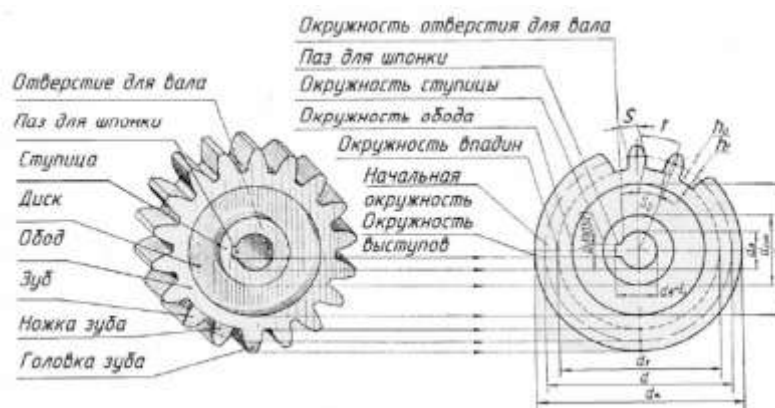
Условные изображения элементов зубчатого колеса
